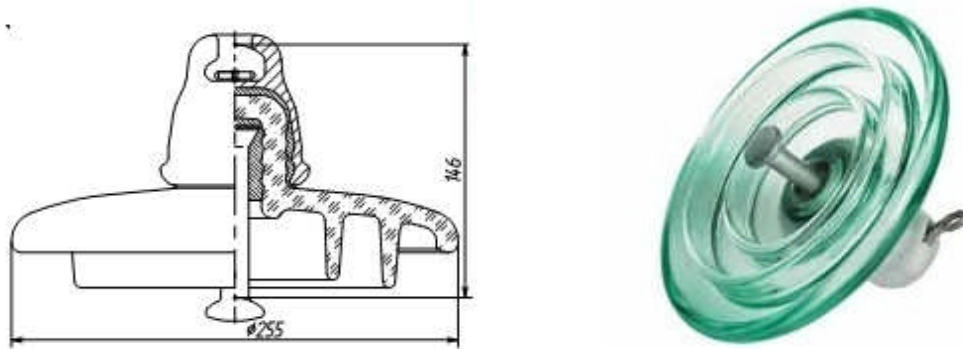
Principales dimensions et forme de l'isolateur U 120B [20]
